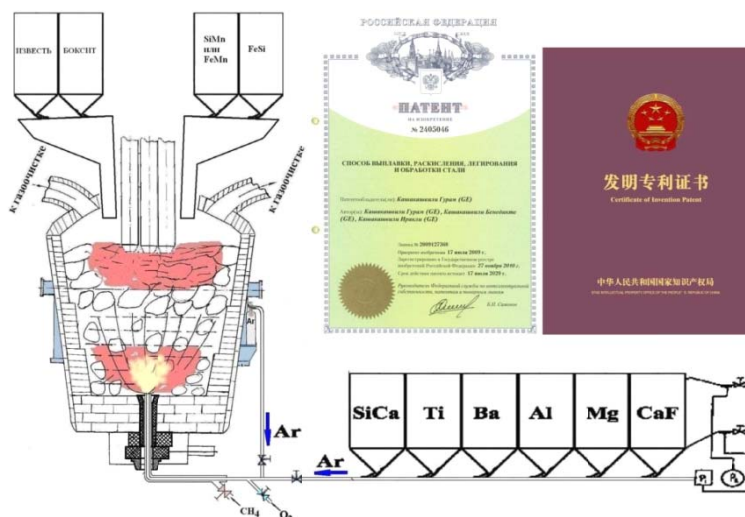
Одношиберный агрегат для совмещения технологии выплавки, раскисления и обработки стали
